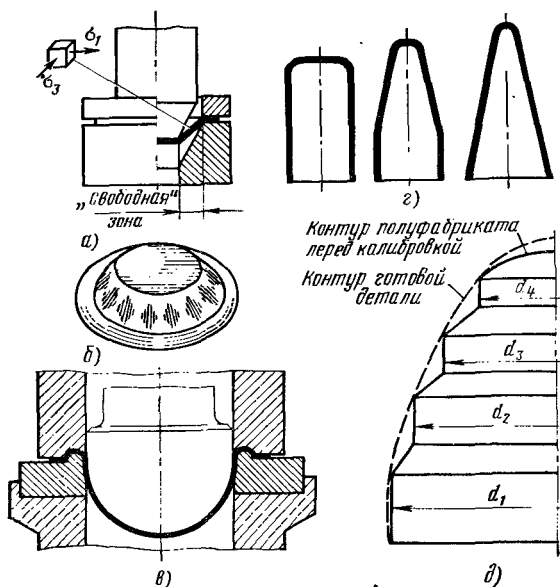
Вытяжка куполообразных нецилиндрических деталей:
